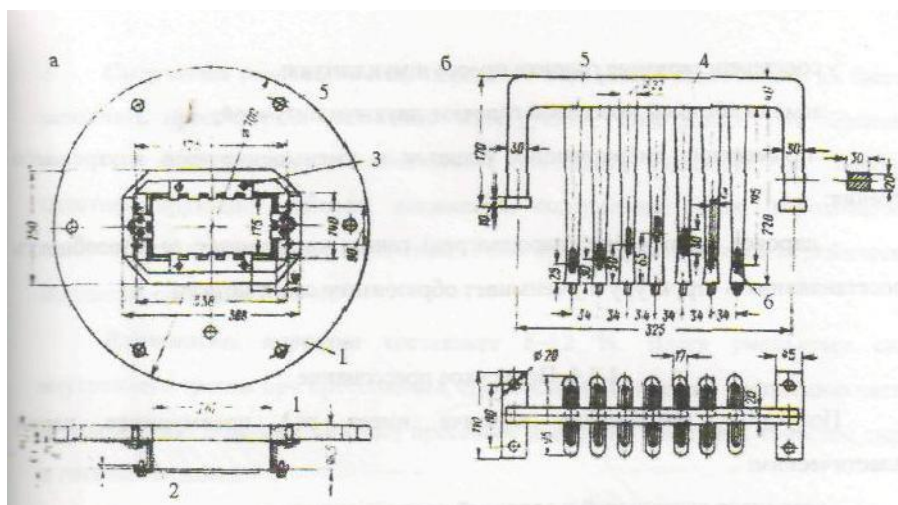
Мундштук для формования семищелевых камней: а - вид с торца и горизонтальный разрез; б - скоба с кернами; 1 - мундштучная плита; 2 - корпус мундштука; 3 - гребень для рифления поверхности; 4 - скоба; 5 - керн о держатели (стержни); 6 – керны
